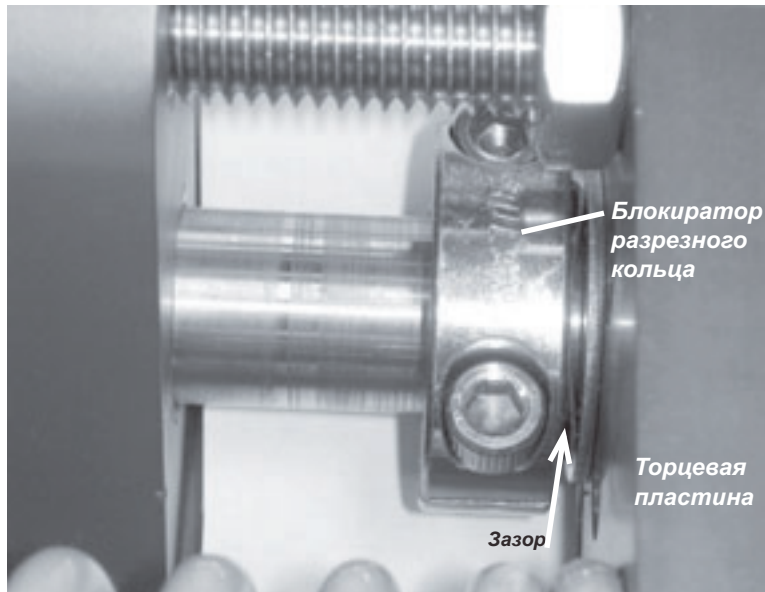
При наличии промежутка между блокиратором разрезного кольца и торцевой пластиной может потребоваться отрегулировать суппорт для закрывания просвета.
